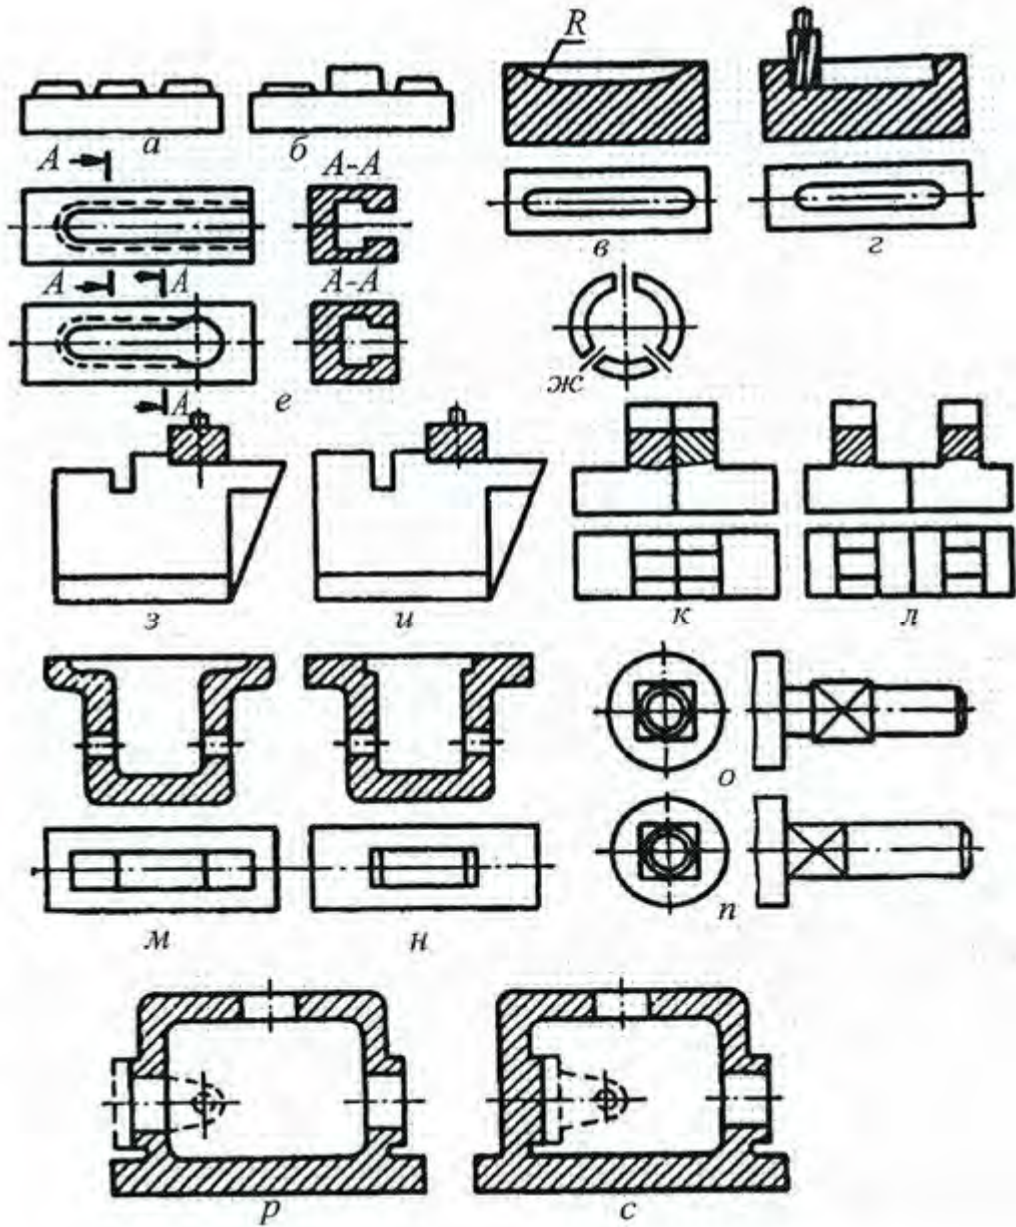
Приклади конструкцій деталей машин, оброблених на фрезерних верстатах
